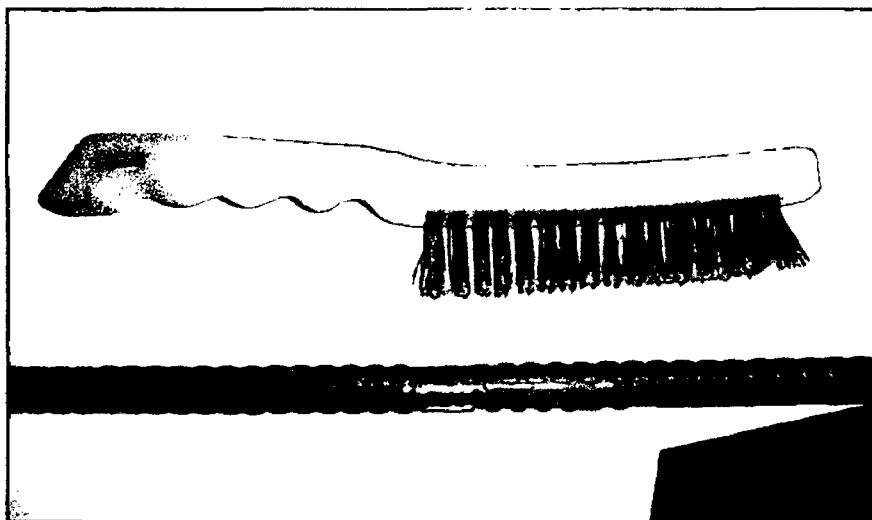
Proceso de limpieza de escoria de soldadura con escobilla con cerdas de acero.
